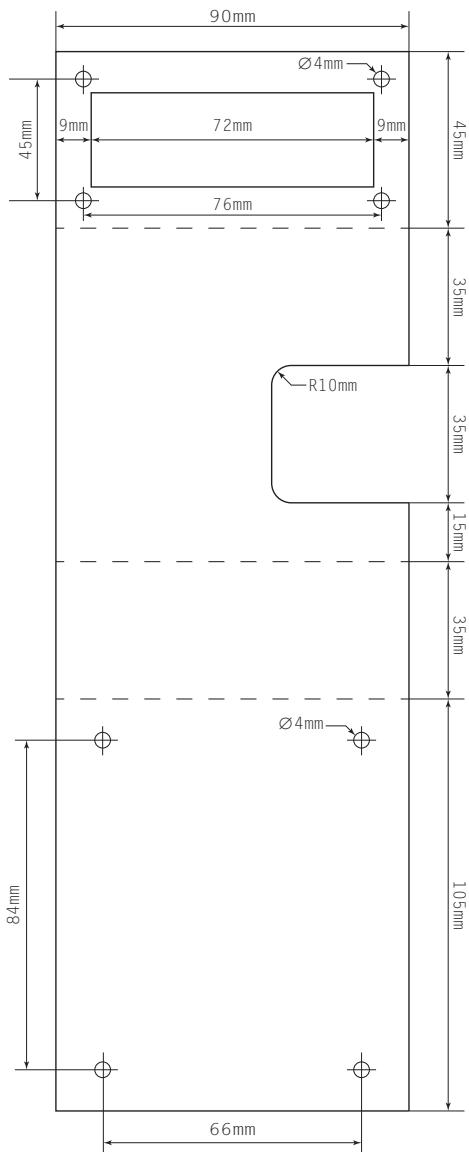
DISEÑO DEL CORTE DEL CHASIS DEL MÓDULO INTERIOR
